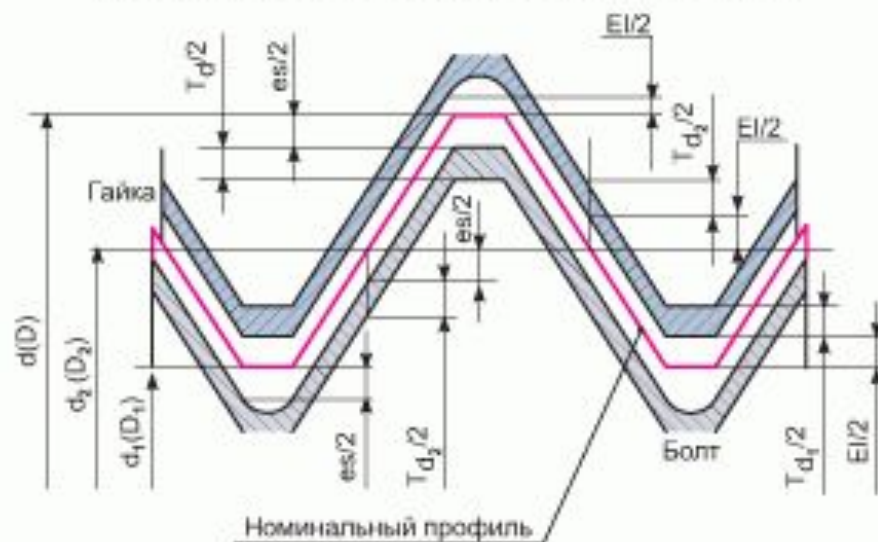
Расположение полей допусков метрической резьбы при посадке с зазором
